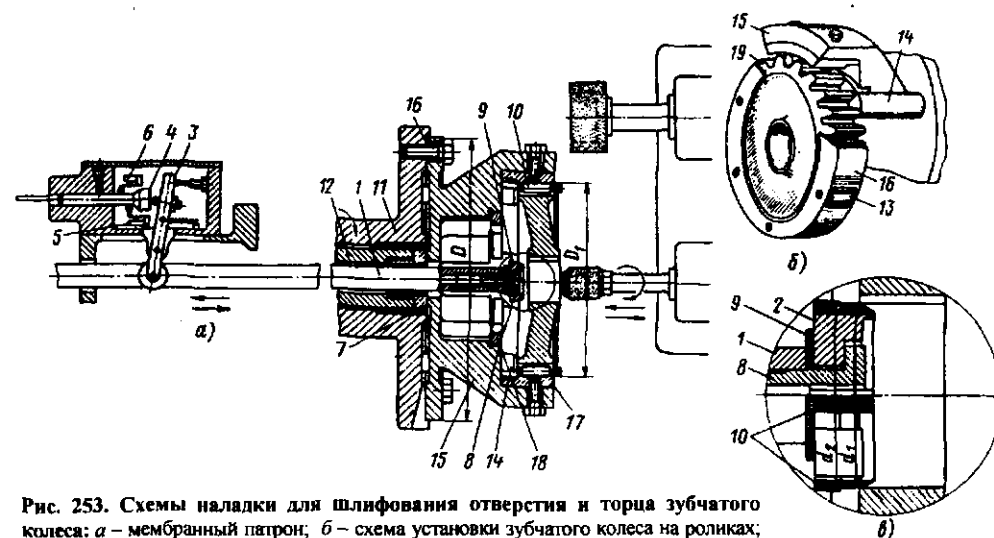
Схемы наладки для шлифования отверстия и торца зубчатого колеса: а – мембранный патрон; б – схема установки зубчатого колеса на роликах; в – схема измерения обрабатываемого отверстия автокалибром
